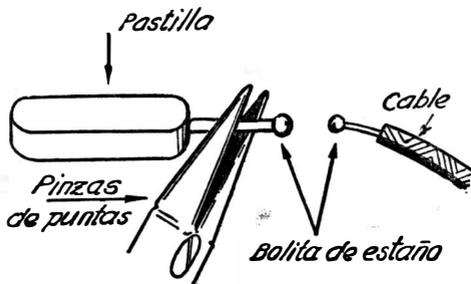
Forma de soldar el cable al terminal del fonocaptor.
